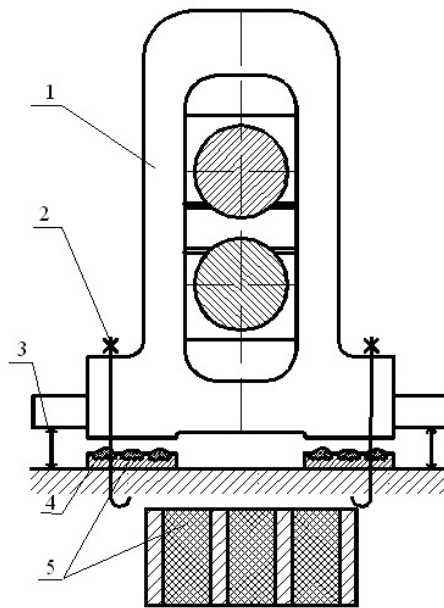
Схема монтажу кліті блюмінгу на плитовини: 1 – кліть, 2 – болти кріплення кліті до фундаменту, 3 – гідродократи, 4 – металополімер, 5 – плитовини
